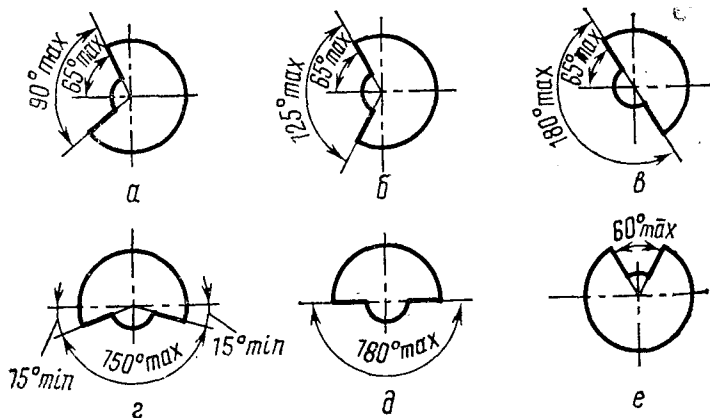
Допускаемые углы раскрытия защитных кожухов, изменяемых на станках:
